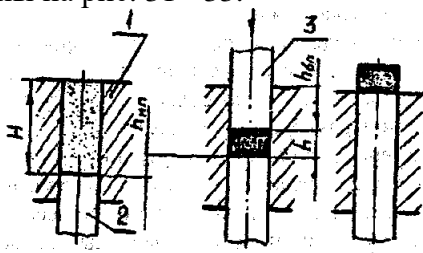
Схема пресс-формы: 1 - верхний пуансон; 2 - матрица; 3 - нижний пуансон; 4 – порошок
